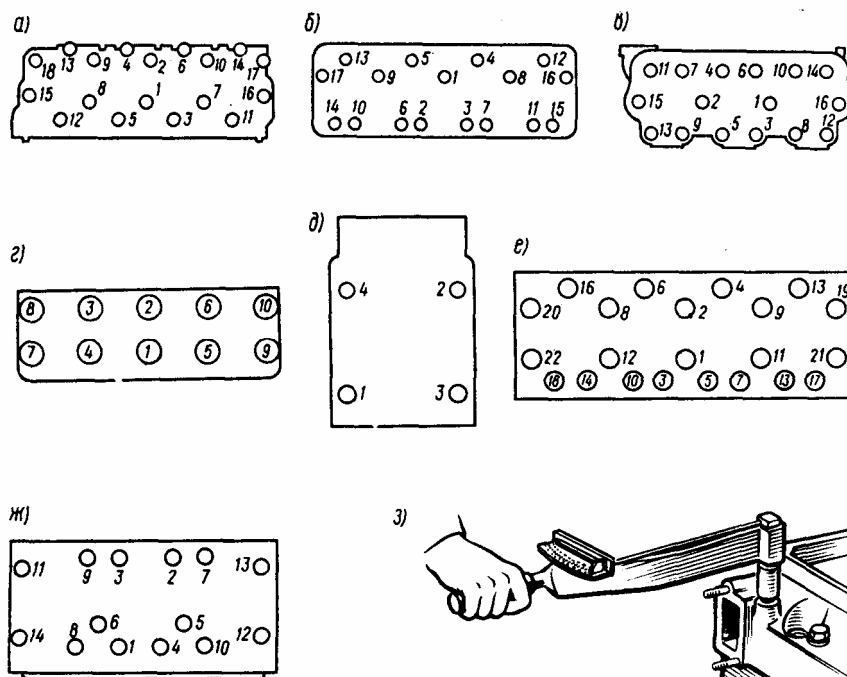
Порядок затяжки болтов (гаек) крепления головки блока цилиндров двигателей автомобилей:
